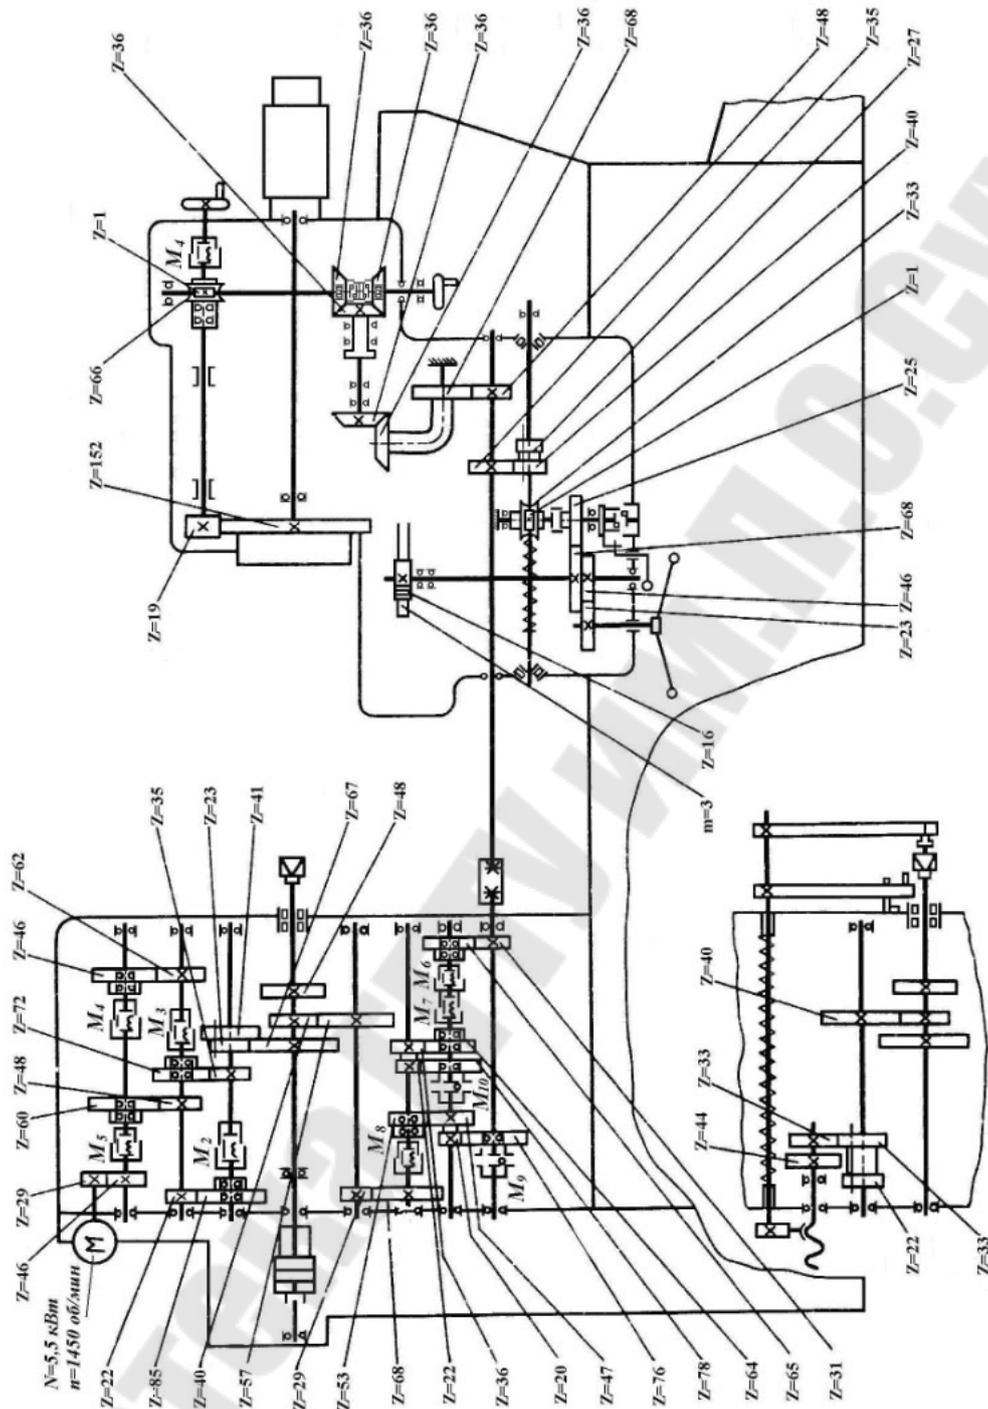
Кинематическая схема токарно-револьверного станка 1К341
